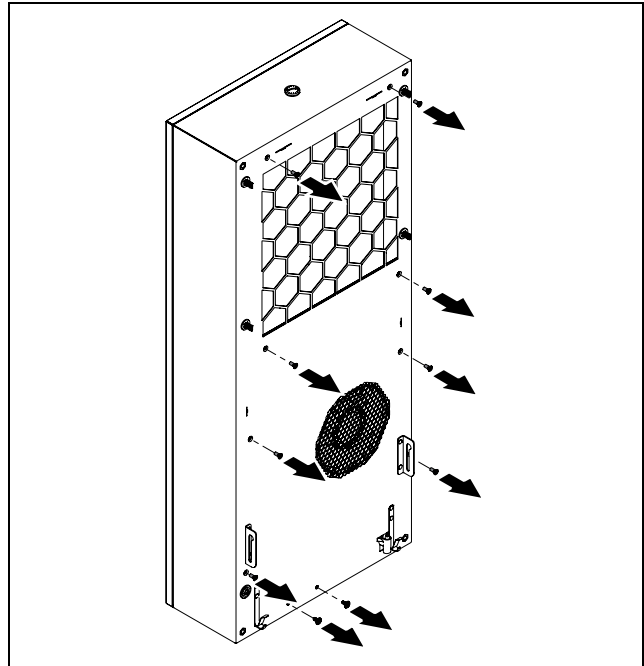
Lösen der Befestigungsschrauben (für SK 34848x0)
